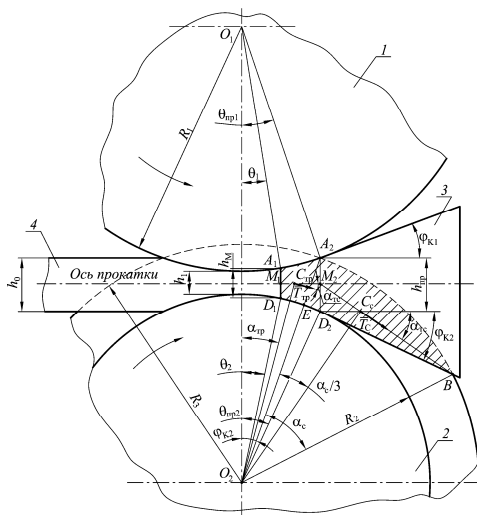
Общий вид устройства для совмещенной прокатки-прессования [4]: 1 – рабочий валок с выступом; 2 – рабочий валок с вырезом; 3 – матрица; 4 – заготовка; 5 – профиль
